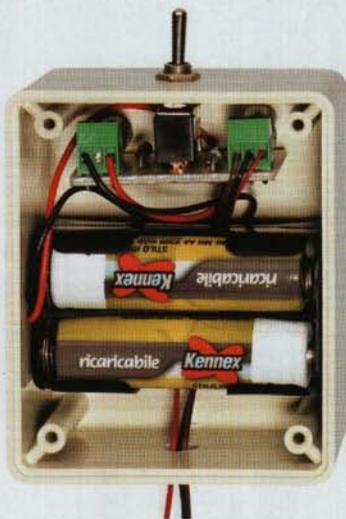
Photo du boîtier ouvert, montage terminé, juste avant de refermer le couvercle.
